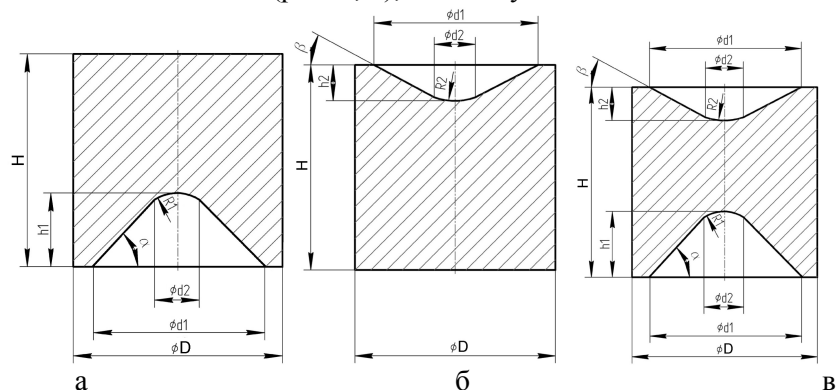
Заготовки с облегчающими полостями: а – нижняя; б – верхняя; в – нижняя и верхняя
